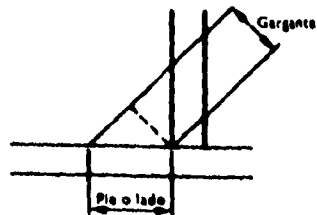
GARGANTA Y PIE DEL CORDON DE UNA SOLDADURA EN ANGULO
